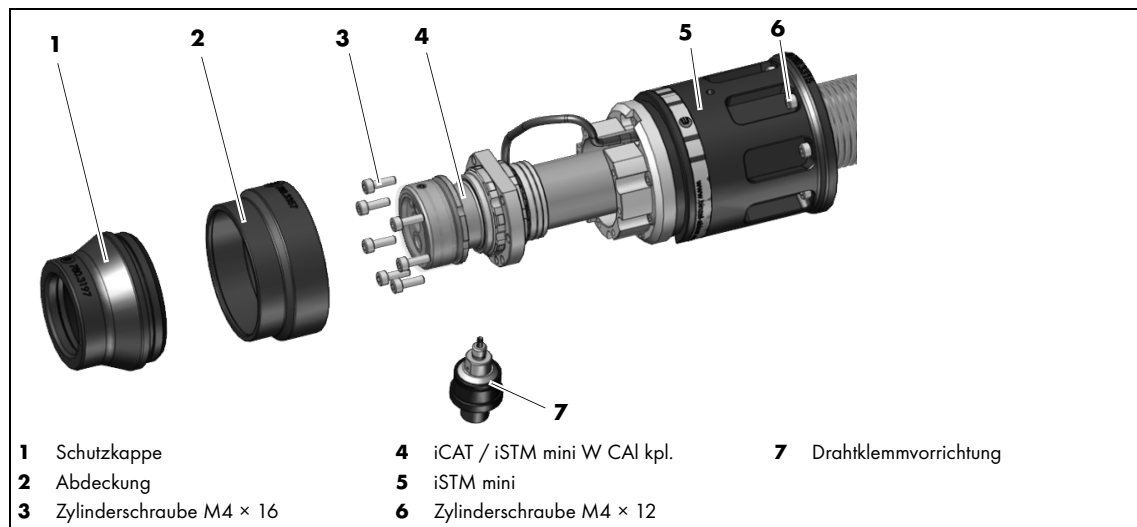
Lieferumfang iSTM mini für ABIROB® W mit Wire-Brake
